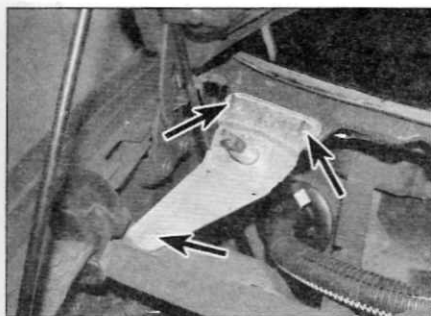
, а. Выверните болты/отверните гайки (отмечены стрелками) крепления крайней оси в сборе...
